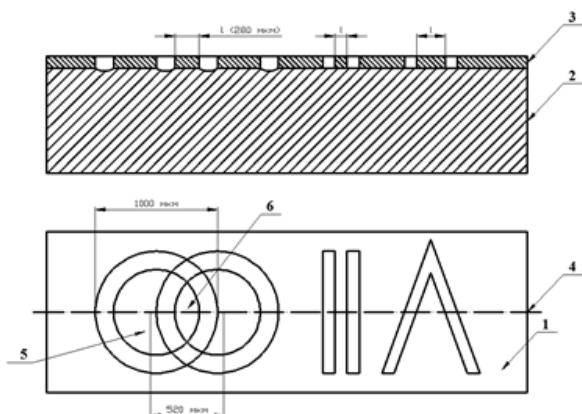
Вид возможных прорезей поверхностного слоя с получением разных по размерам площадок покрытия. 1 – образец (изделие), 2 – подложка, 3 – тонкое покрытие, 4 – ось смещения трубчатого сверла, 5 – площадка покрытия с большим размером, 6 – площадка покрытия с меньшим размером
